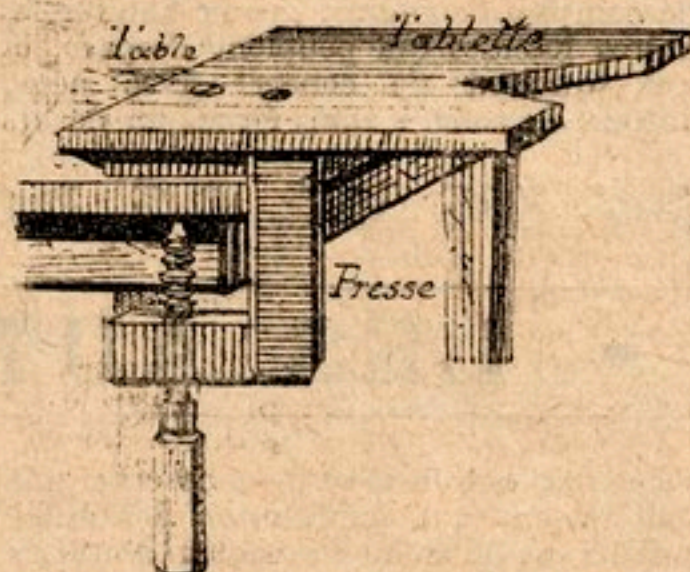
Planchette fixée sur une presse à bois et serrée sur le bord d'une table.
